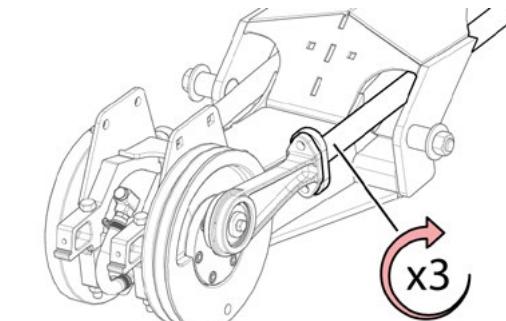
Затяните правый рычаг привода ножа на 3 оборота
